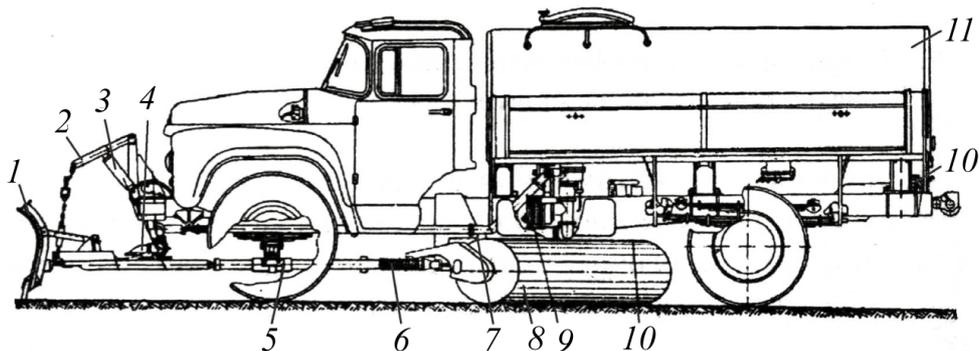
Поливомоечная машина: 1 – плужный рабочий орган; 2 – механизм подъема; 3 – гидроцилиндр; 4 – шарнирные моечные сопла насадок; 5 – кран управления; 6 – толкающая рама; 7 – трубопровод; 8 – щетка с ворсом; 9 – насосная установка ПН-1200А; 10 – кран-разобщитель; 11 – цистерна
